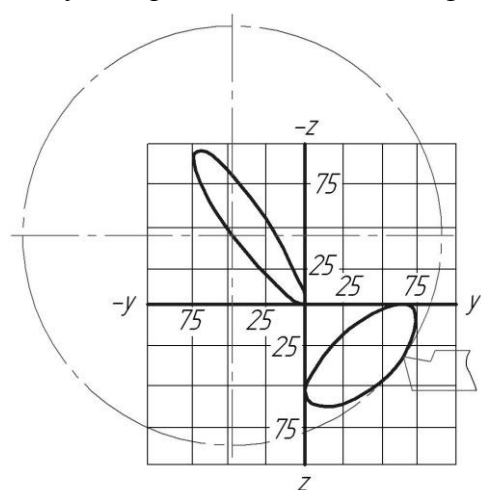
Траектории движения резца и заготовки при точении с колебаниями [3]
